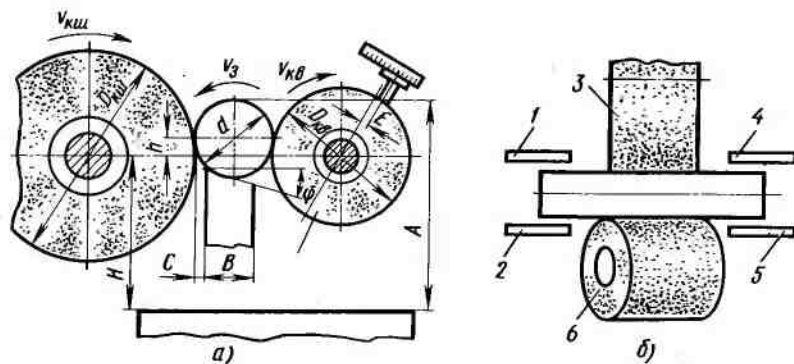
Схемы наладки бесцентрово-шлифовального станка:
